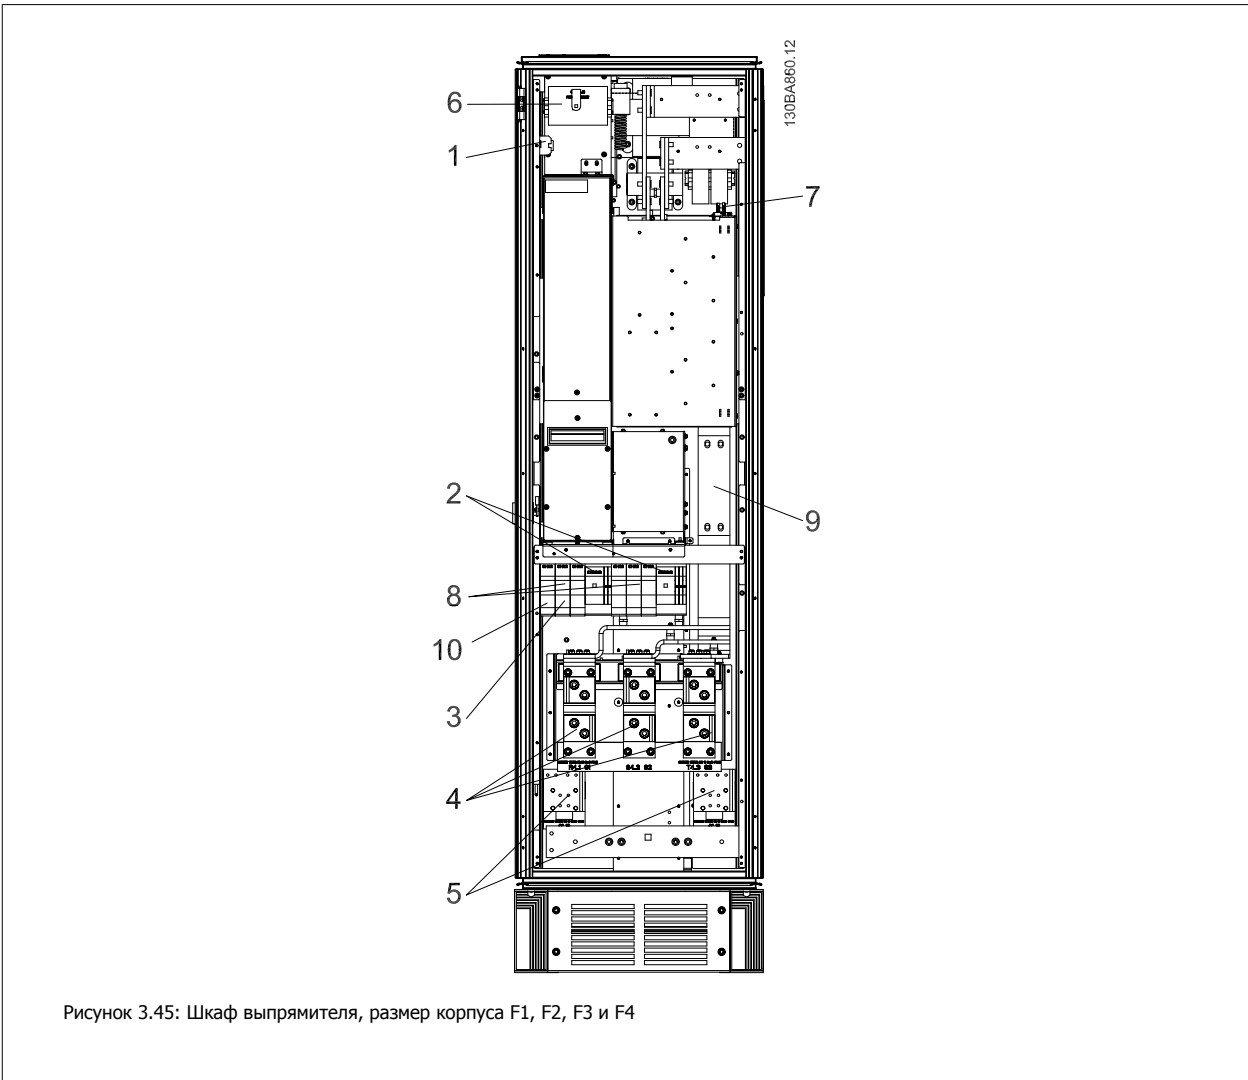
Шкаф выпрямителя, размер корпуса F1, F2, F3 и F4
